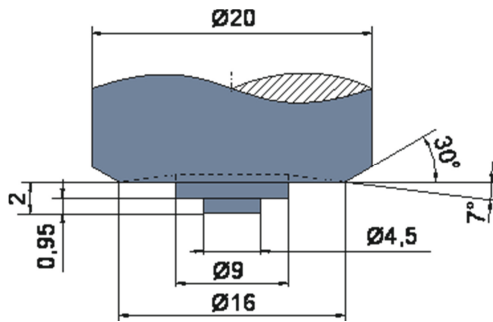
Breites Werkzeug für Gusslegierung
